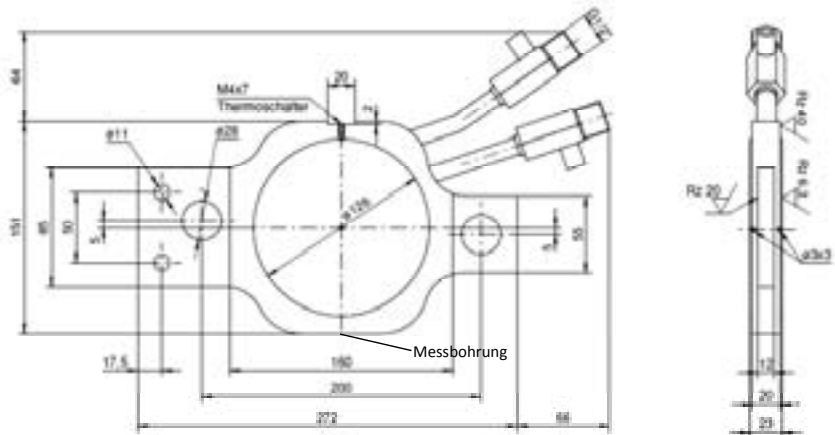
Kühlkörper für Presspacks mit Kontaktdurchmesser bis 125mm
